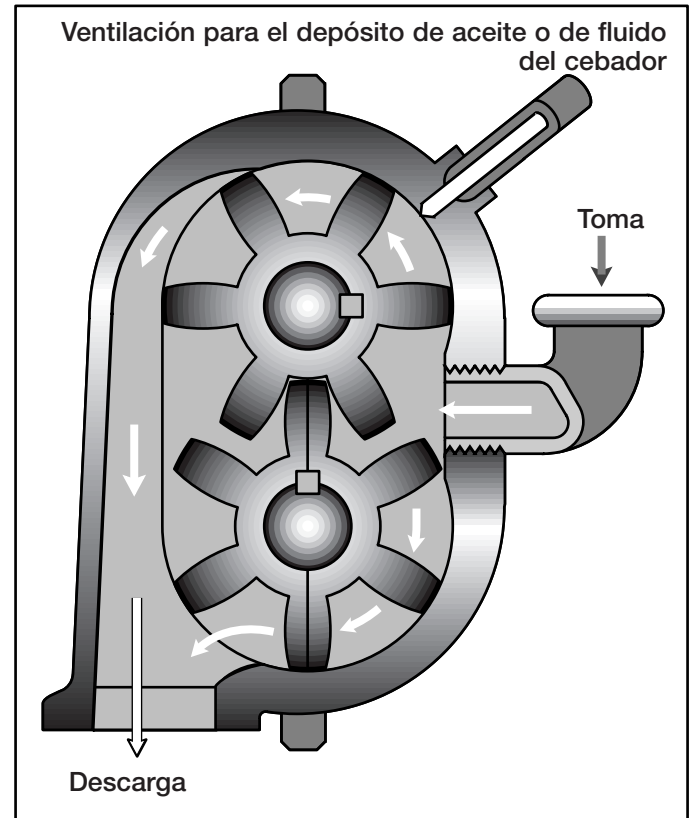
Diseño básico de una bomba de engranajes rotatorios.
